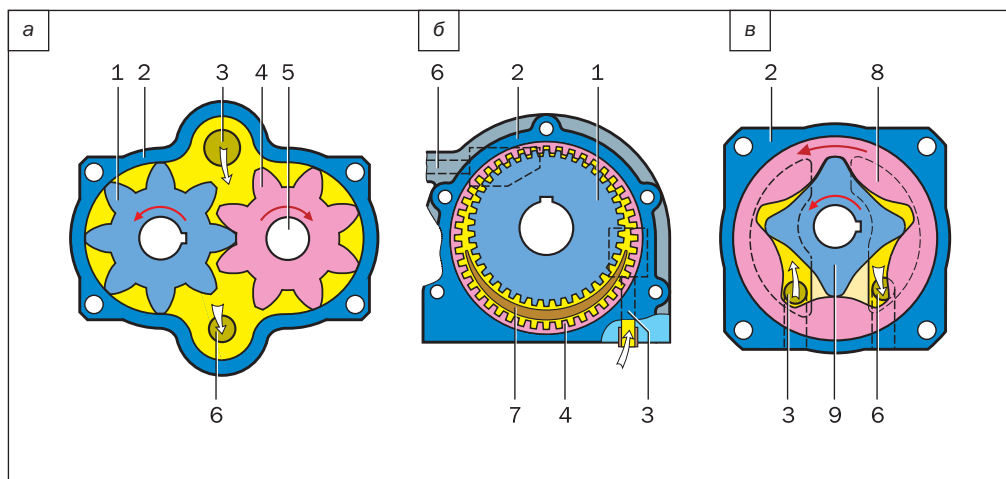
Схемы масляных насосов: а — шестеренный с наружным зацеплением; б — шестеренный с внутренним зацеплением; в — роторный; 1 — ведущая шестерня; 2 — корпус насоса; 3 — всасывающий канал; 4 — ведомая шестерня; 5 — ось; 6 — нагнетательный канал; 7 — разделительный сектор; 8 — ведомый ротор; 9 — ведущий ротор
